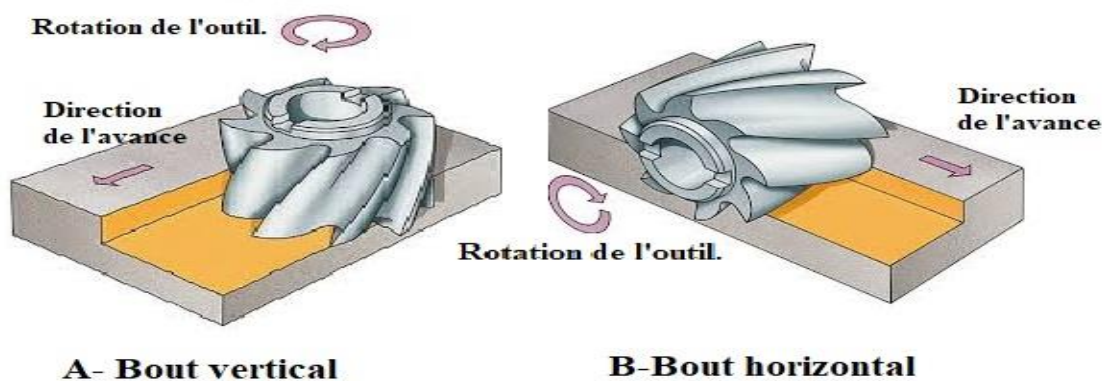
Fraisage en bout vertical et bout horizontal [4].
